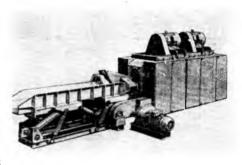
Двухроторный окорочно-зачистной станок 20К40-1
